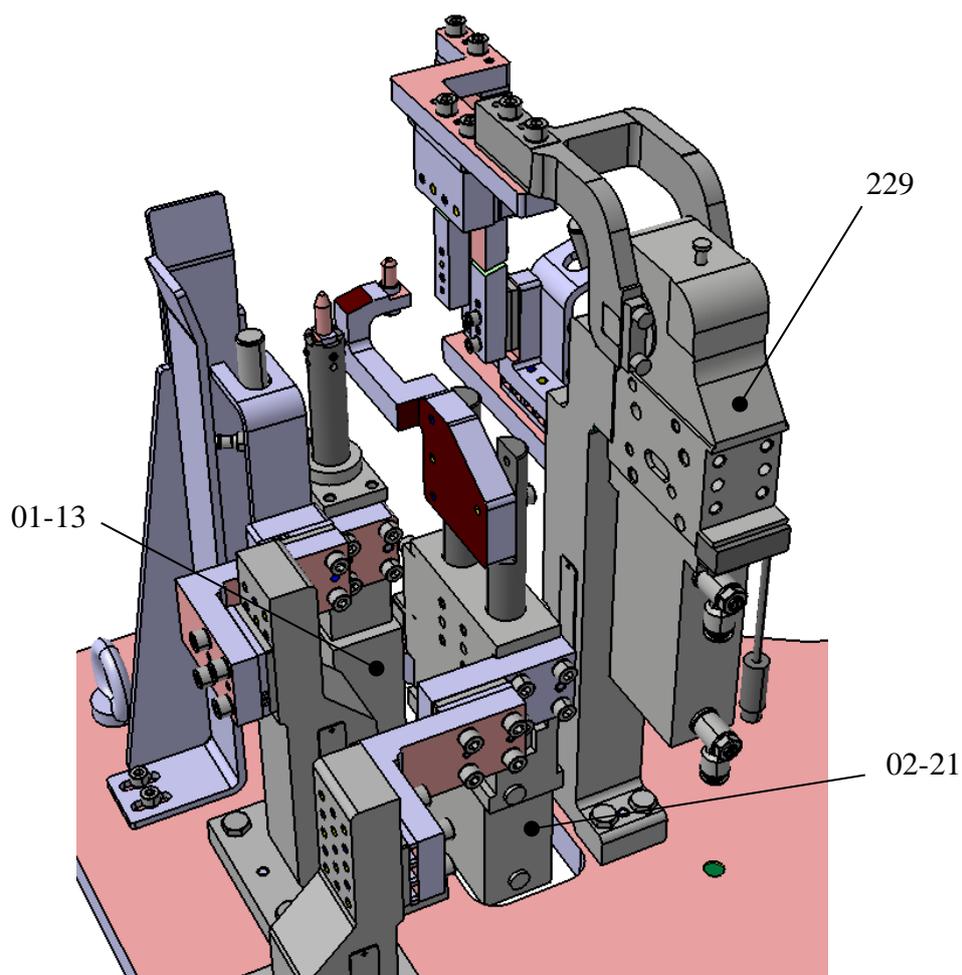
Маркировка пневматических механизмов для сварочной станции
